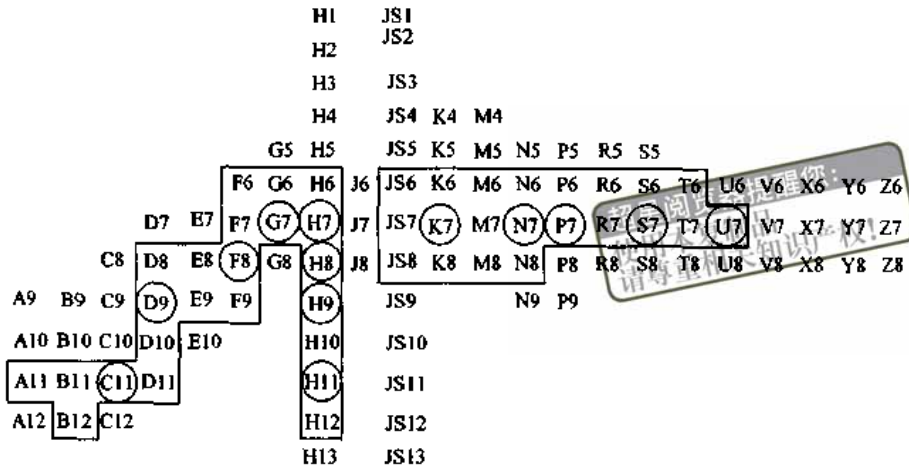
基本尺寸至 500mm 的孔公差带
